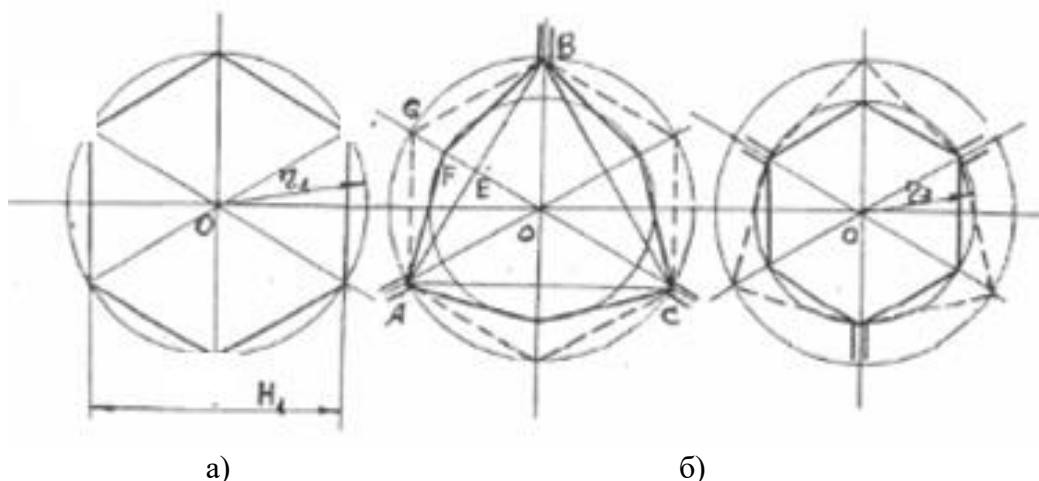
Исходная заготовка (а) и схема двух калибров (б) РКБ
